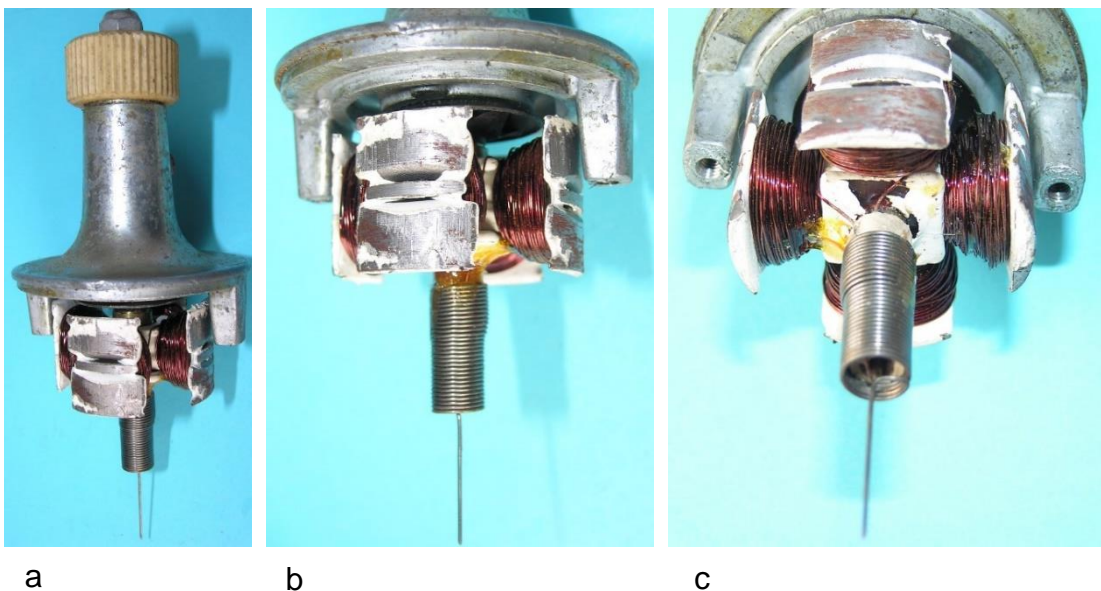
Metamorphose des Schleifrings zur Schleifnadel: a) Lagerhals mit Anker, b) Befestigung der Schleifnadel auf der Welle mit einer Schraubenfeder, c) Schraubenfeder mit Schleifdraht (axialauslaufendes Federende)
